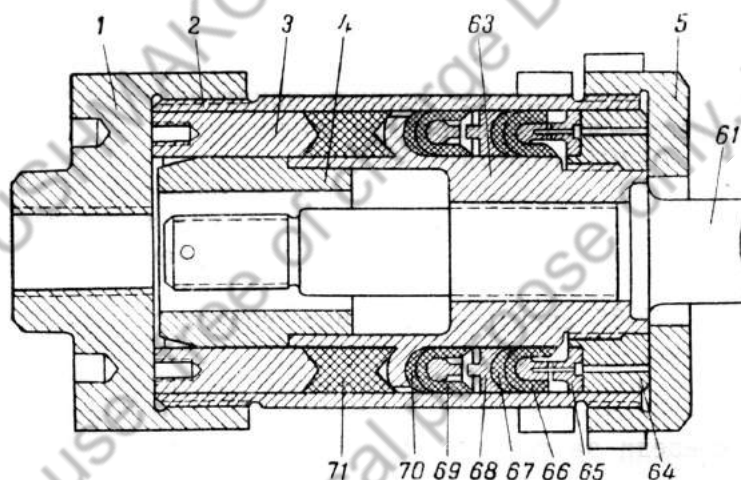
Сборка поршня штока накатника при помощи прибора (*сб.* 42-18):
